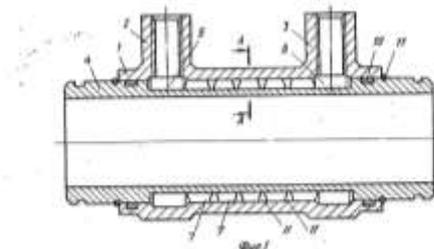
Подогреватель биотоплива: 1-корпус; 2-подводящая трубка; 3-отводящая трубка; 4-корпус теплоносителя; 5-подводящая камера; 6-отводящая камера; 7-криволинейные рёбра; 10-уплотнительное кольцо; 11-стопорное кольцо.
